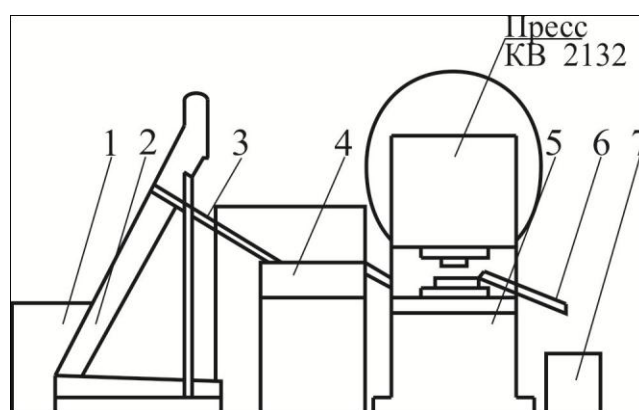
Участок автоматической линии штамповки детали «корпус форсунки»
